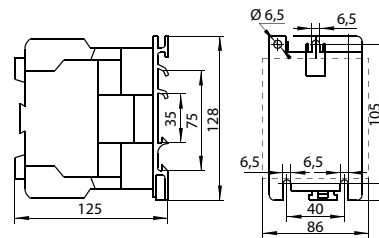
Габаритные размеры пускателя ПМА 5100
